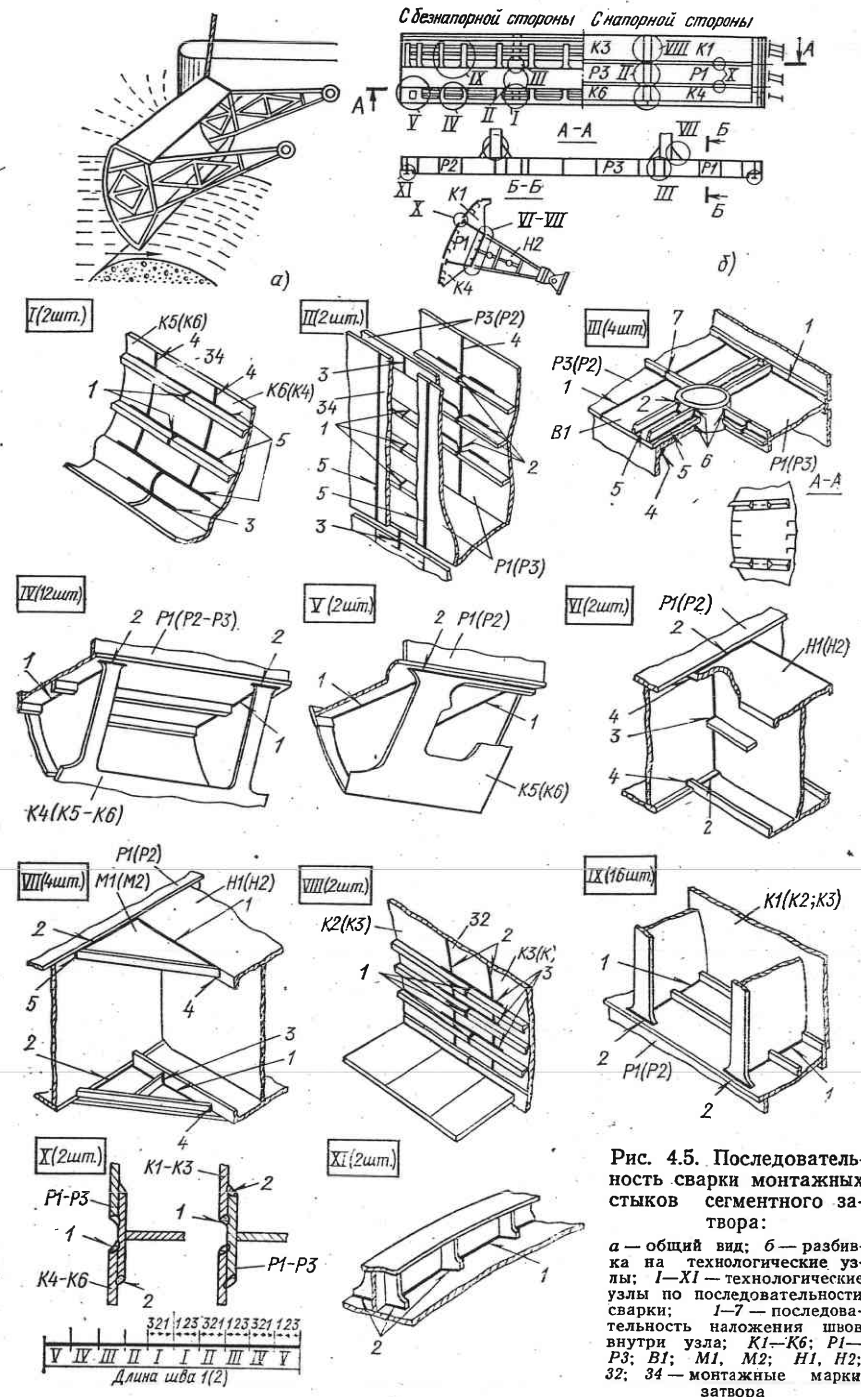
Последовательность сварки монтажных стыков сегментного затвора:
